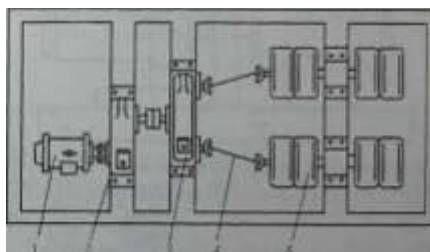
Схема роликового вращателя: 1 - электродвигатель; 2 - редуктор; 3 - распределитель мощности; 4 - вал; 5 - обрезиненный ролик
